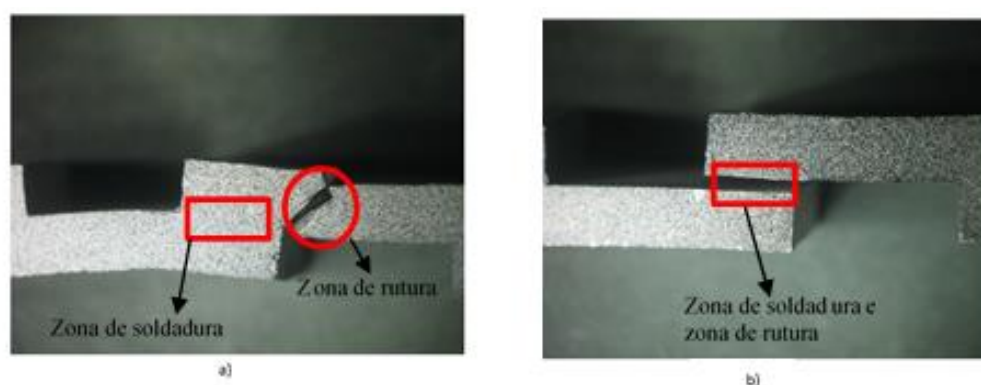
Zona de rutura a) na soldadura (provete AA/CS-ANF25-T1), b) no alumínio (provete AA/CS-ANF25-T3)
